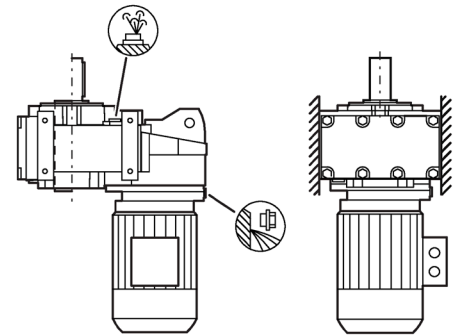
Einbaulagen für Flachgetriebe F.F Flanschführung und F.Z mit Gehäuseflansch, Baugrößen 39 - 189
